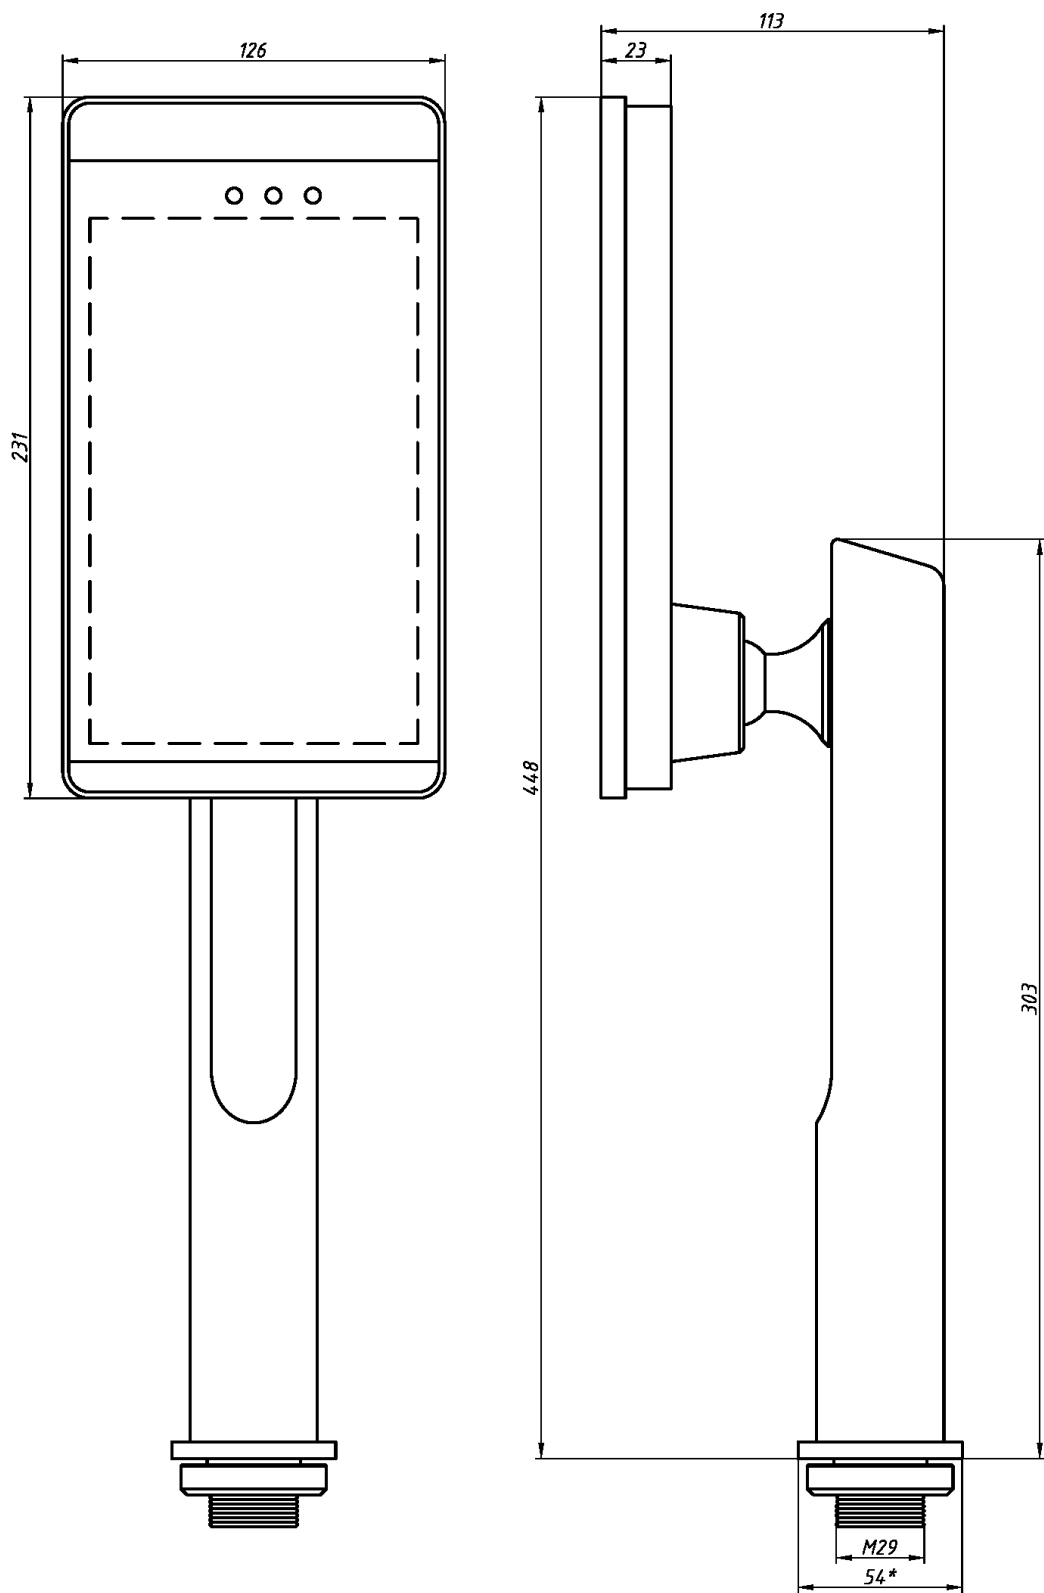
Габаритные размеры и крепёж терминала R20-Face T8”
